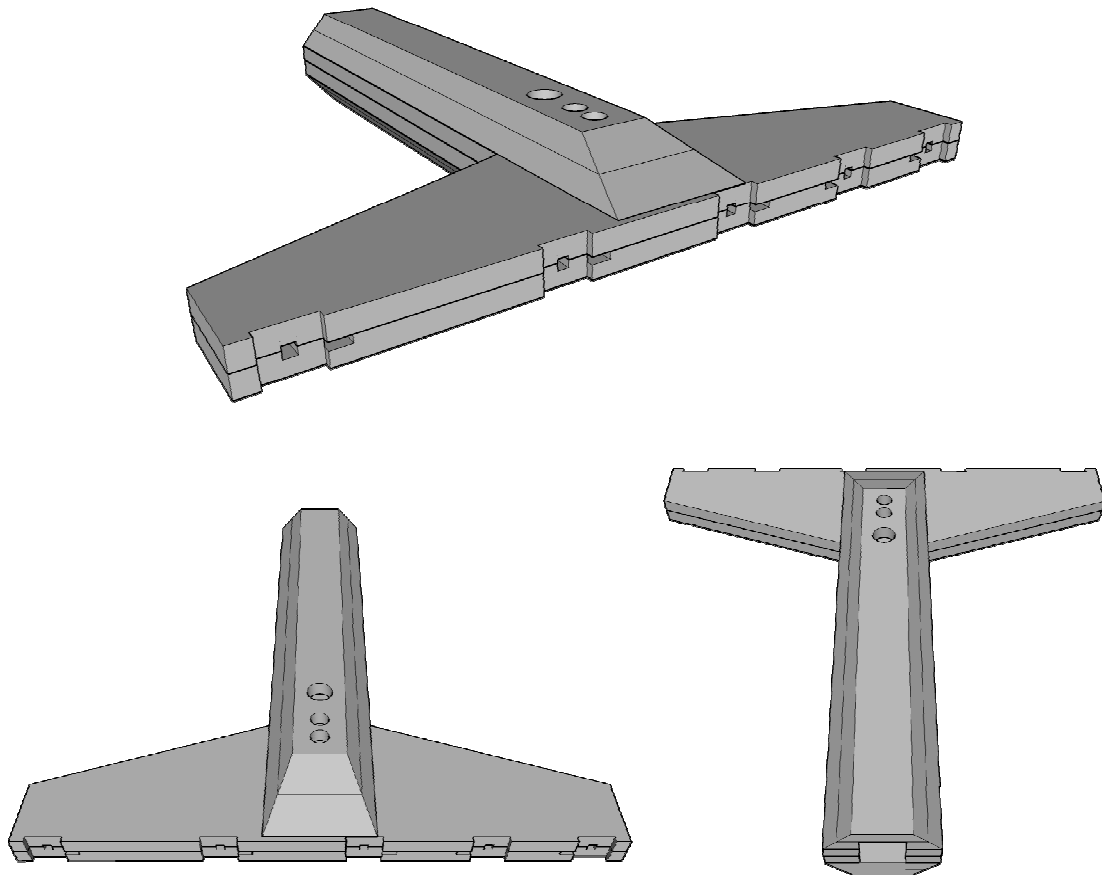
Vistas del diseño de la interfaz mecánica sin componentes.
